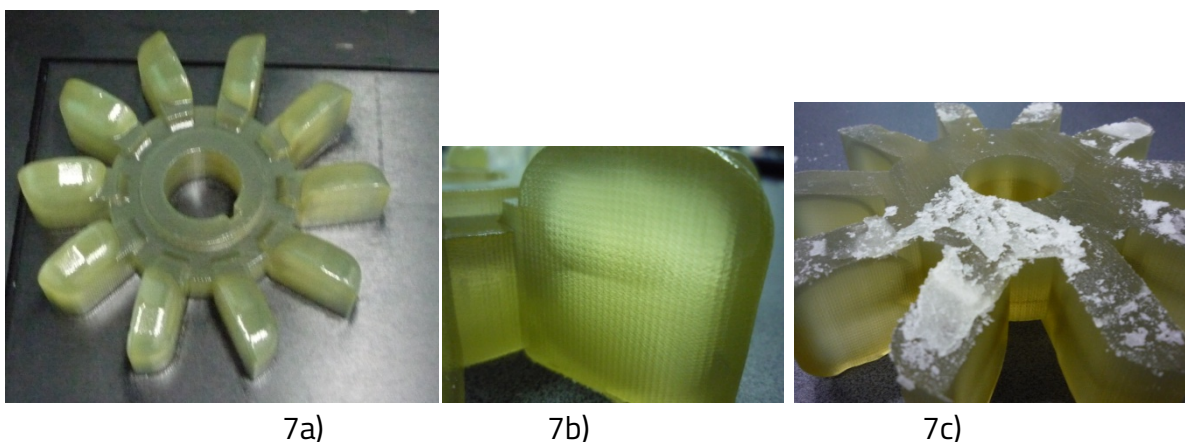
a) Rotorul turbinei Pelton pe platforma de construcție b) Detaliu privind o cupă a rotorului c) Detaliu privind partea inferioară a rotorului cu material suport [27]
